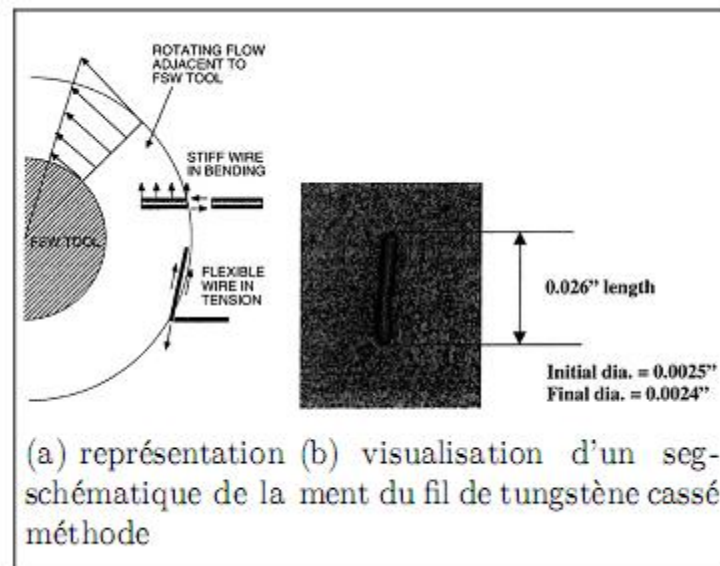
Méthode utilisée par Schneider [Schneider et al .154] pour analyser l'écoulement de la matière pendant le soudage FSW.
